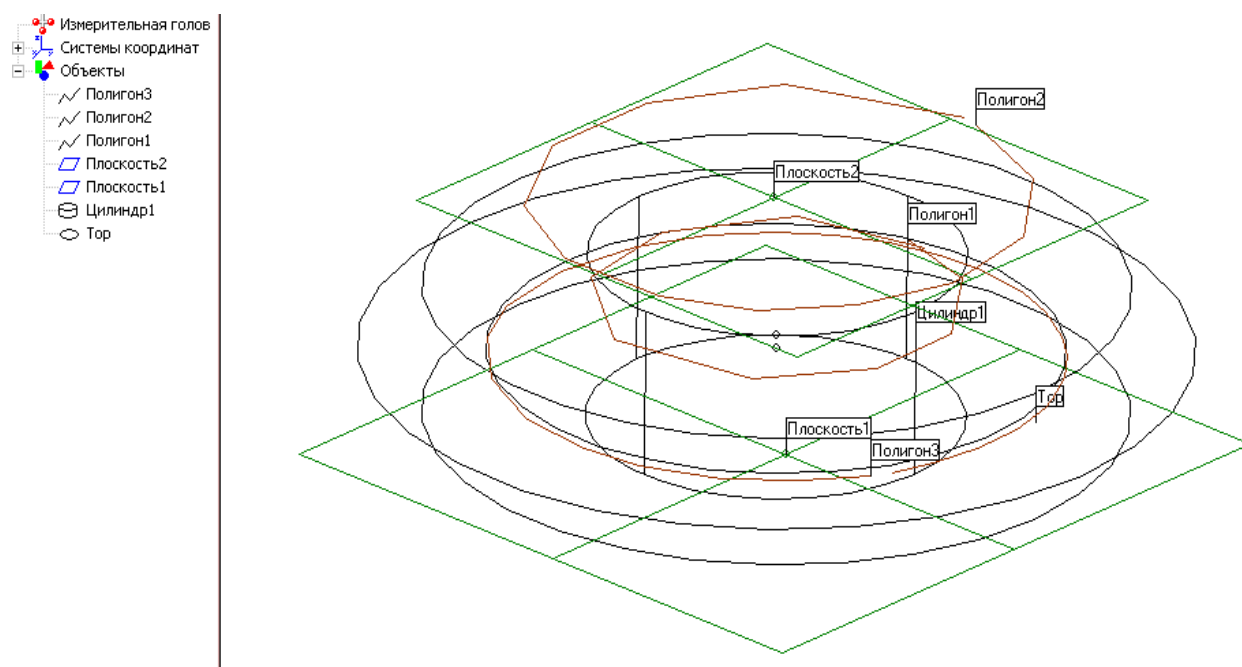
Сеанс вимірювання кільця кульового підшипника
